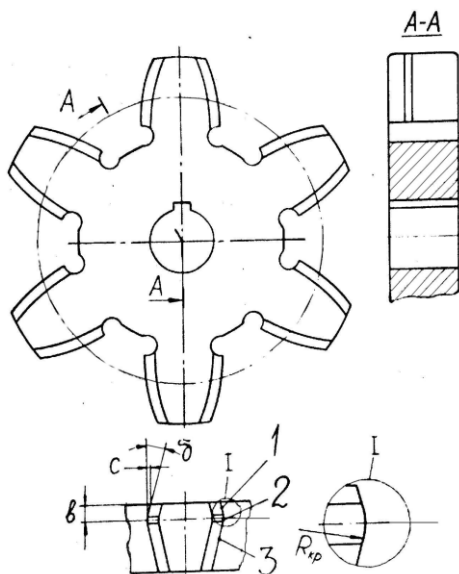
Рабочий чертеж алмазного эластичного хона для окончательной обработки сферического зубчатого колеса с постоянным нормальным шагом
